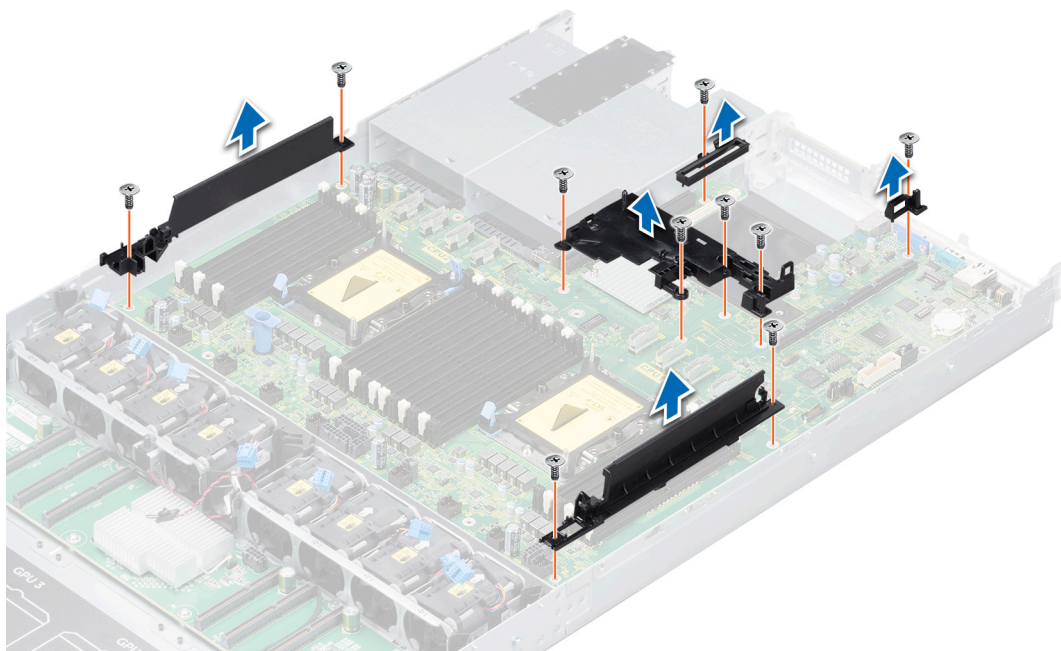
Entfernen Sie die Kabelführungen, die NDC-Führung, die PCIe-Führung und die PCH-Gehäusebasis.
